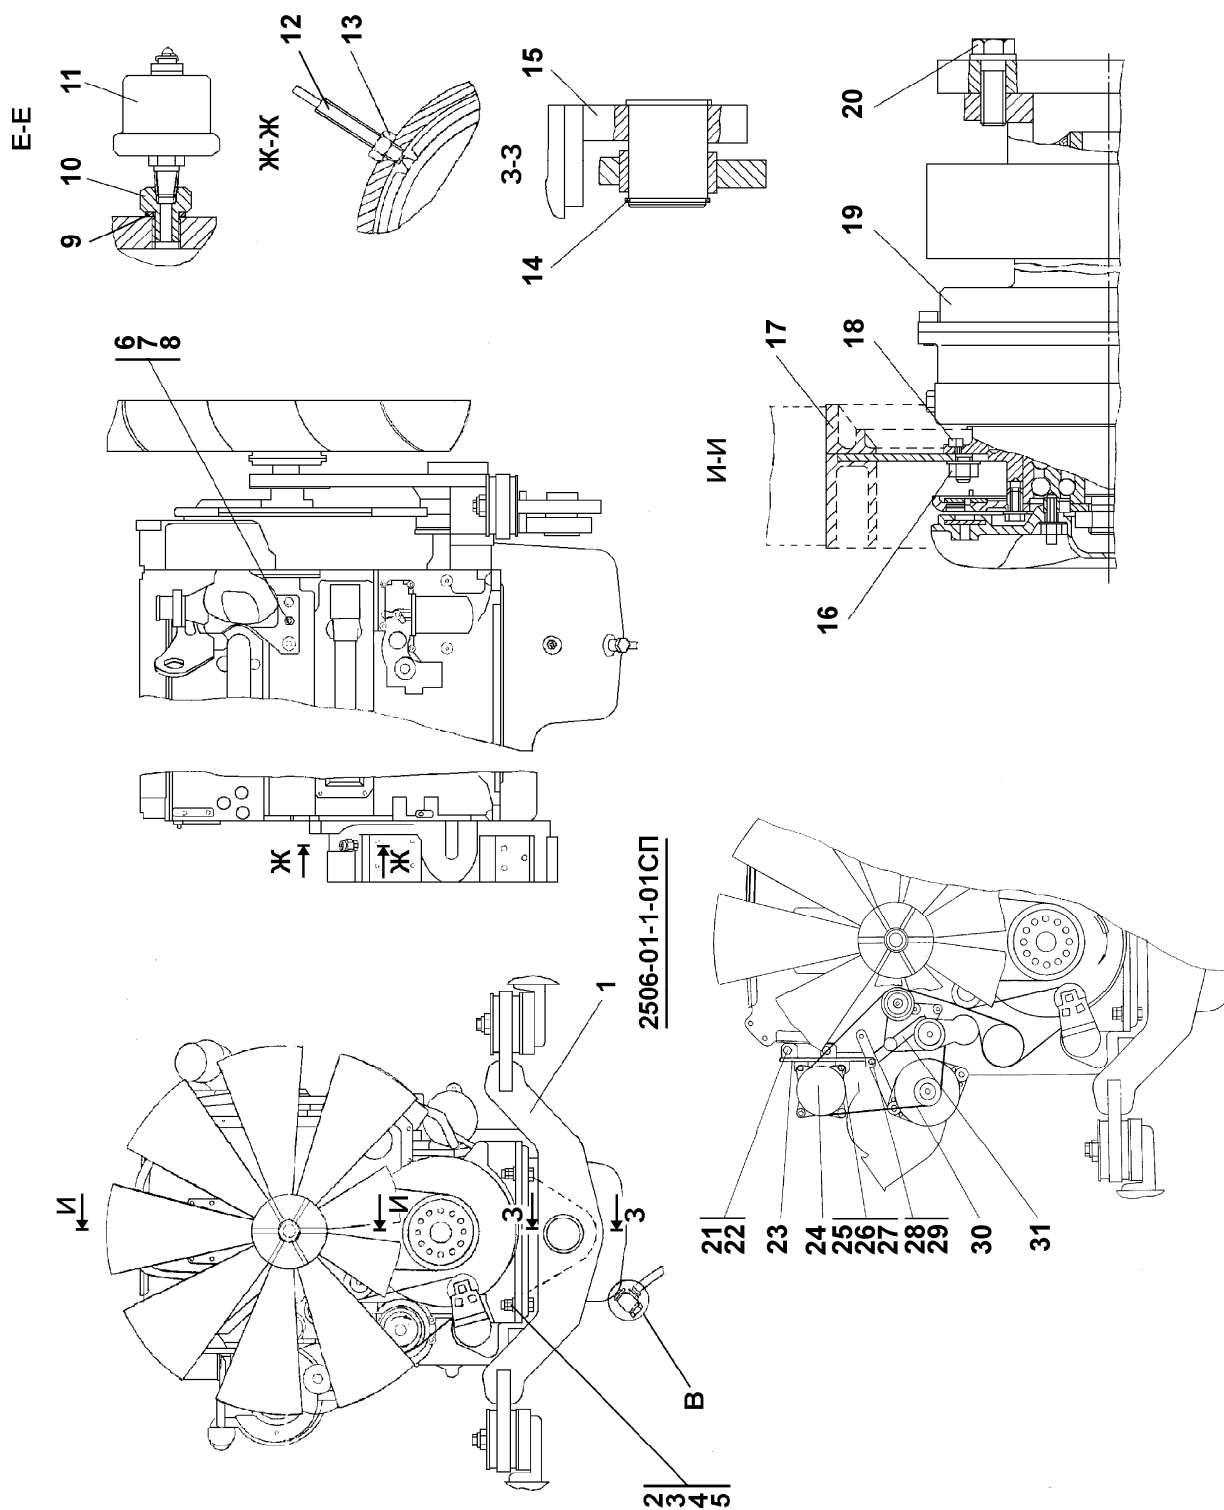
Установка двигателя QSX1-C440 «Cummins»
